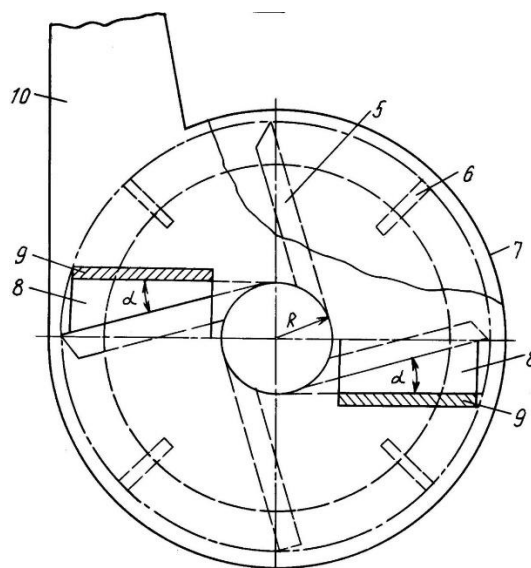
Дисковий подрібнювач: 5 - ніж; 6 - лопатки; 7 - кожух;
